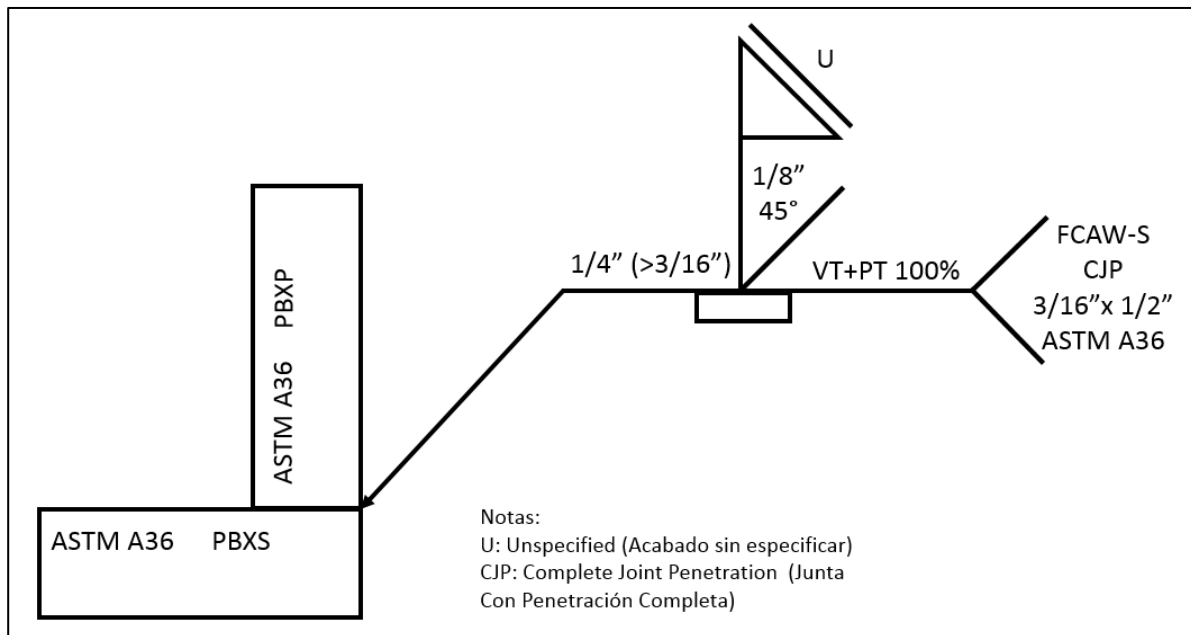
Simbología Para El Proceso De Soldadura De Este Trabajo [64].
